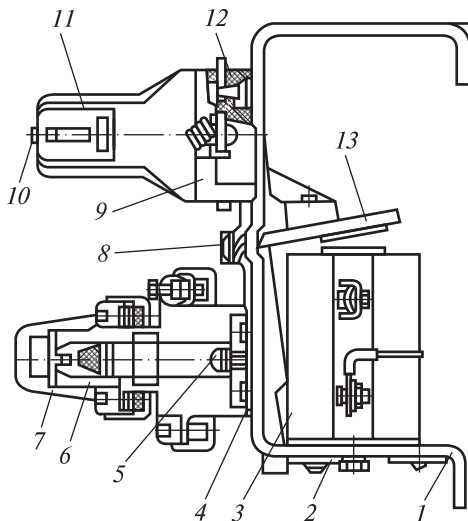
Контактторы типа МК1, МК3: 1 — скоба; 2, 6, 9, 12 — колодки; 3 — катушка; 4 — пластина; 5 — винт; 7, 10 — траверсы; 8 — пружина; 11 — дугогасительная камера; 13 — якорь
